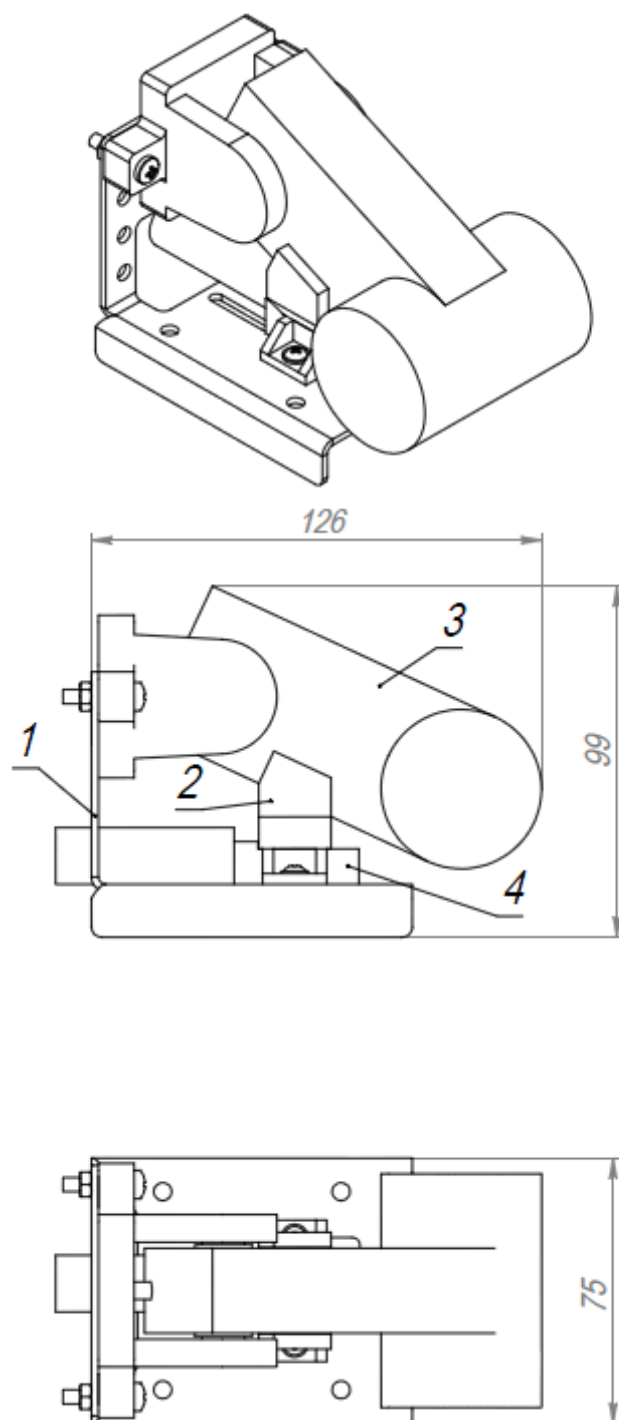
Внешний вид и схема установки датчика проникновения
